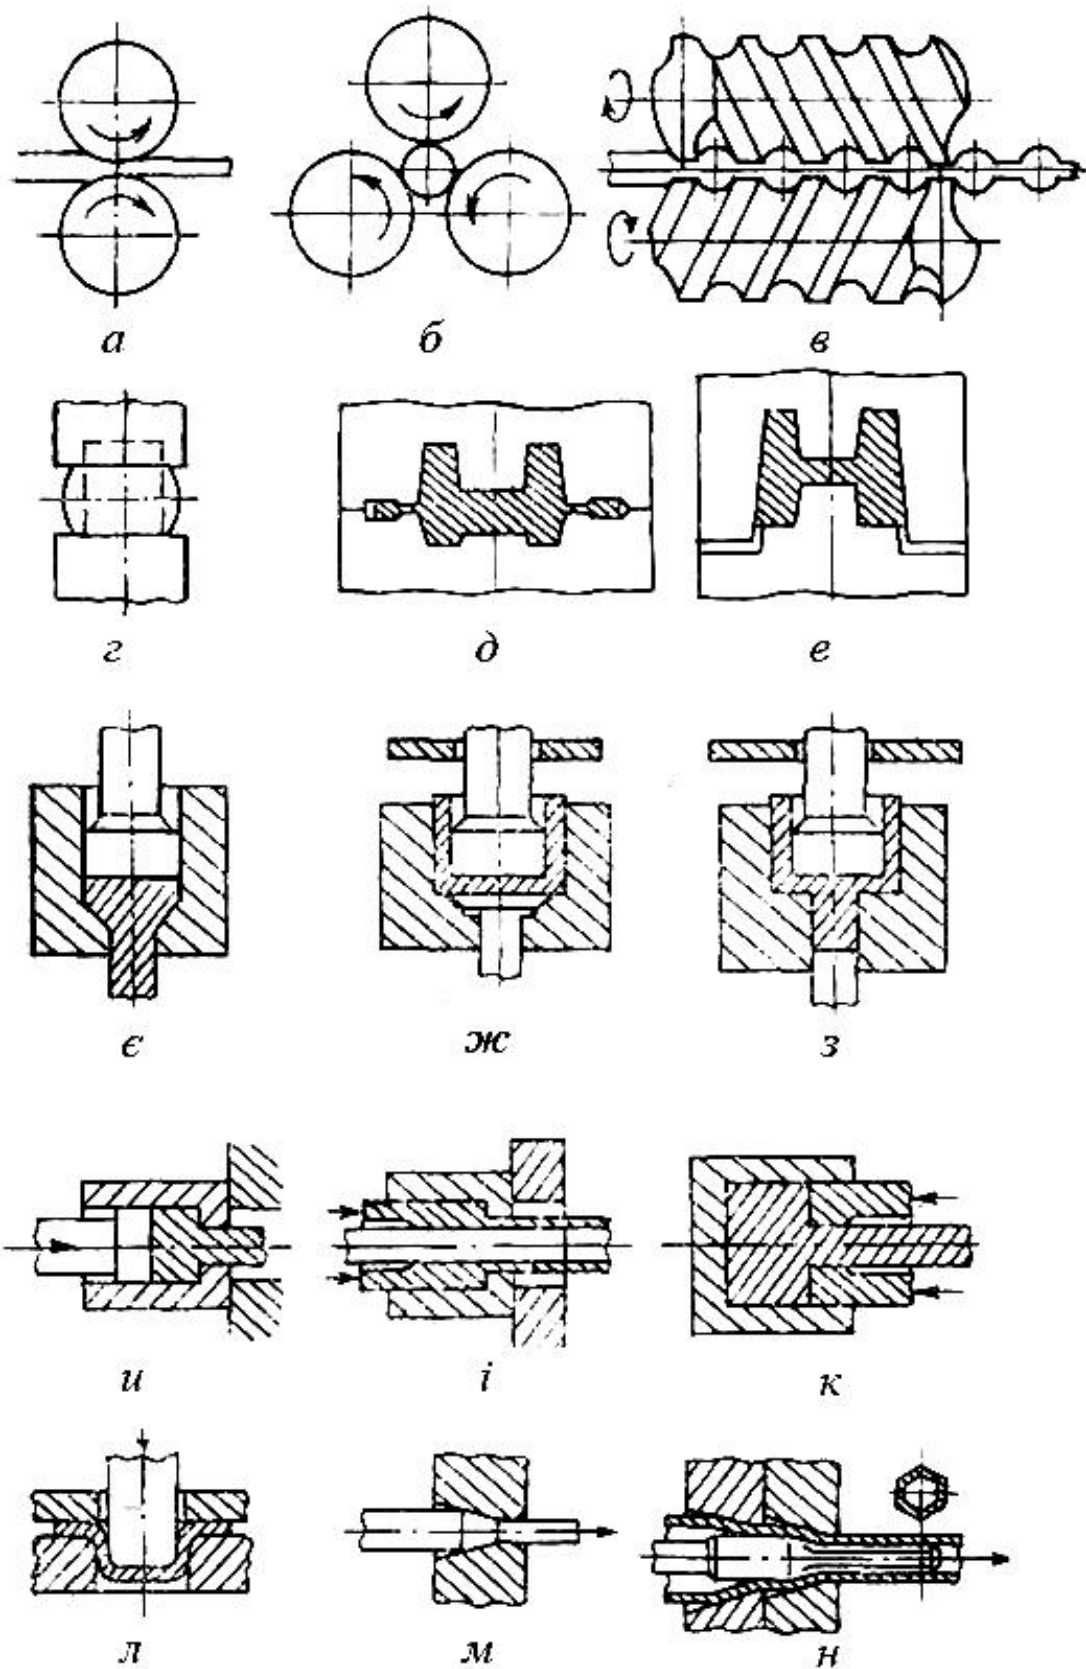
Принципові схеми основних видів оброблення металів тиском
